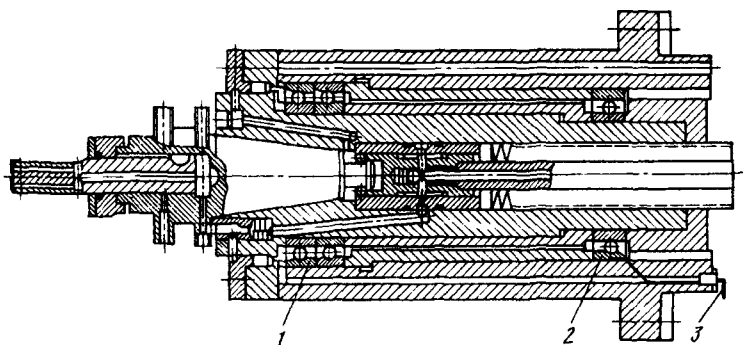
Шпиндель станка, оснащенный датчиками-подшипниками
